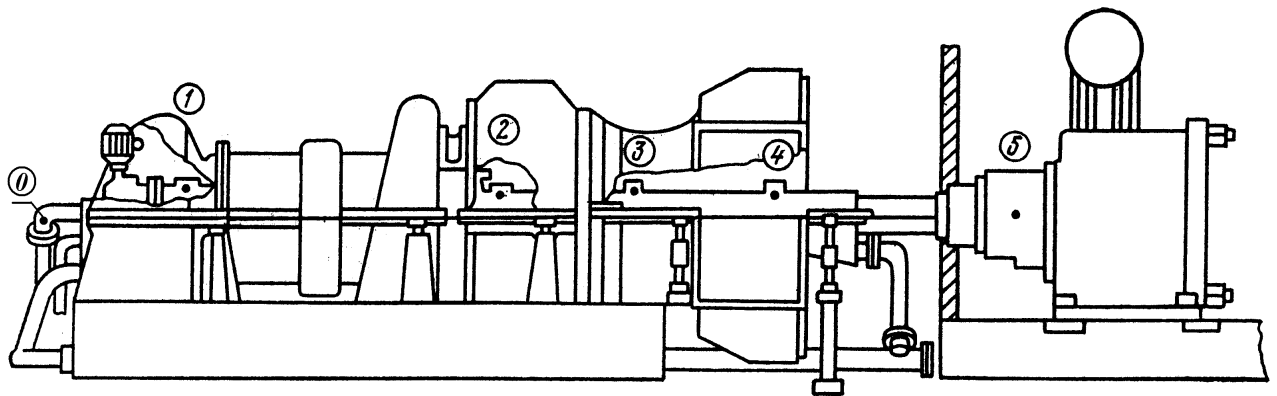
Схема компресора з контрольними точками вимірювання вібрації.
